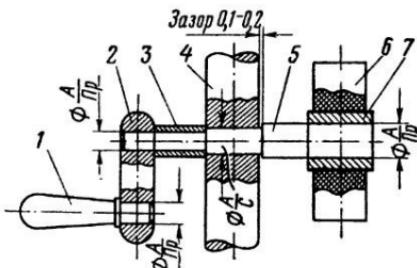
Модель фрикционной передачи с перпендикулярными осями дисков (схема соединения деталей): узел привода (1 — ручка; 2 — рычаг ручки; 3 — упорная втулка; 4 — стойка; 5 — вал привода; 6 — ведущий диск; 7 — металлическая втулка).
